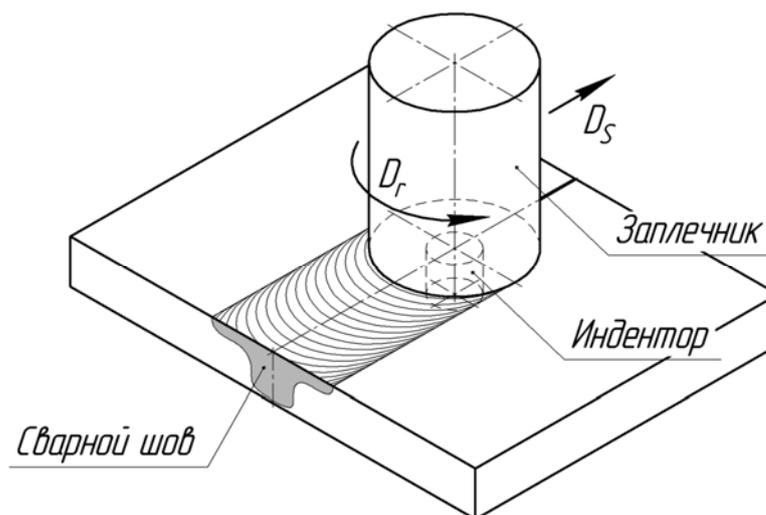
Схема процесса сварки фрикционным перемешиванием.
